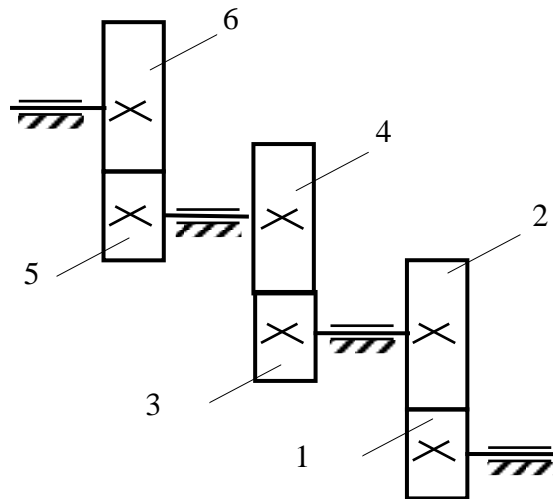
Кинематическая схема зубчатой передачи
